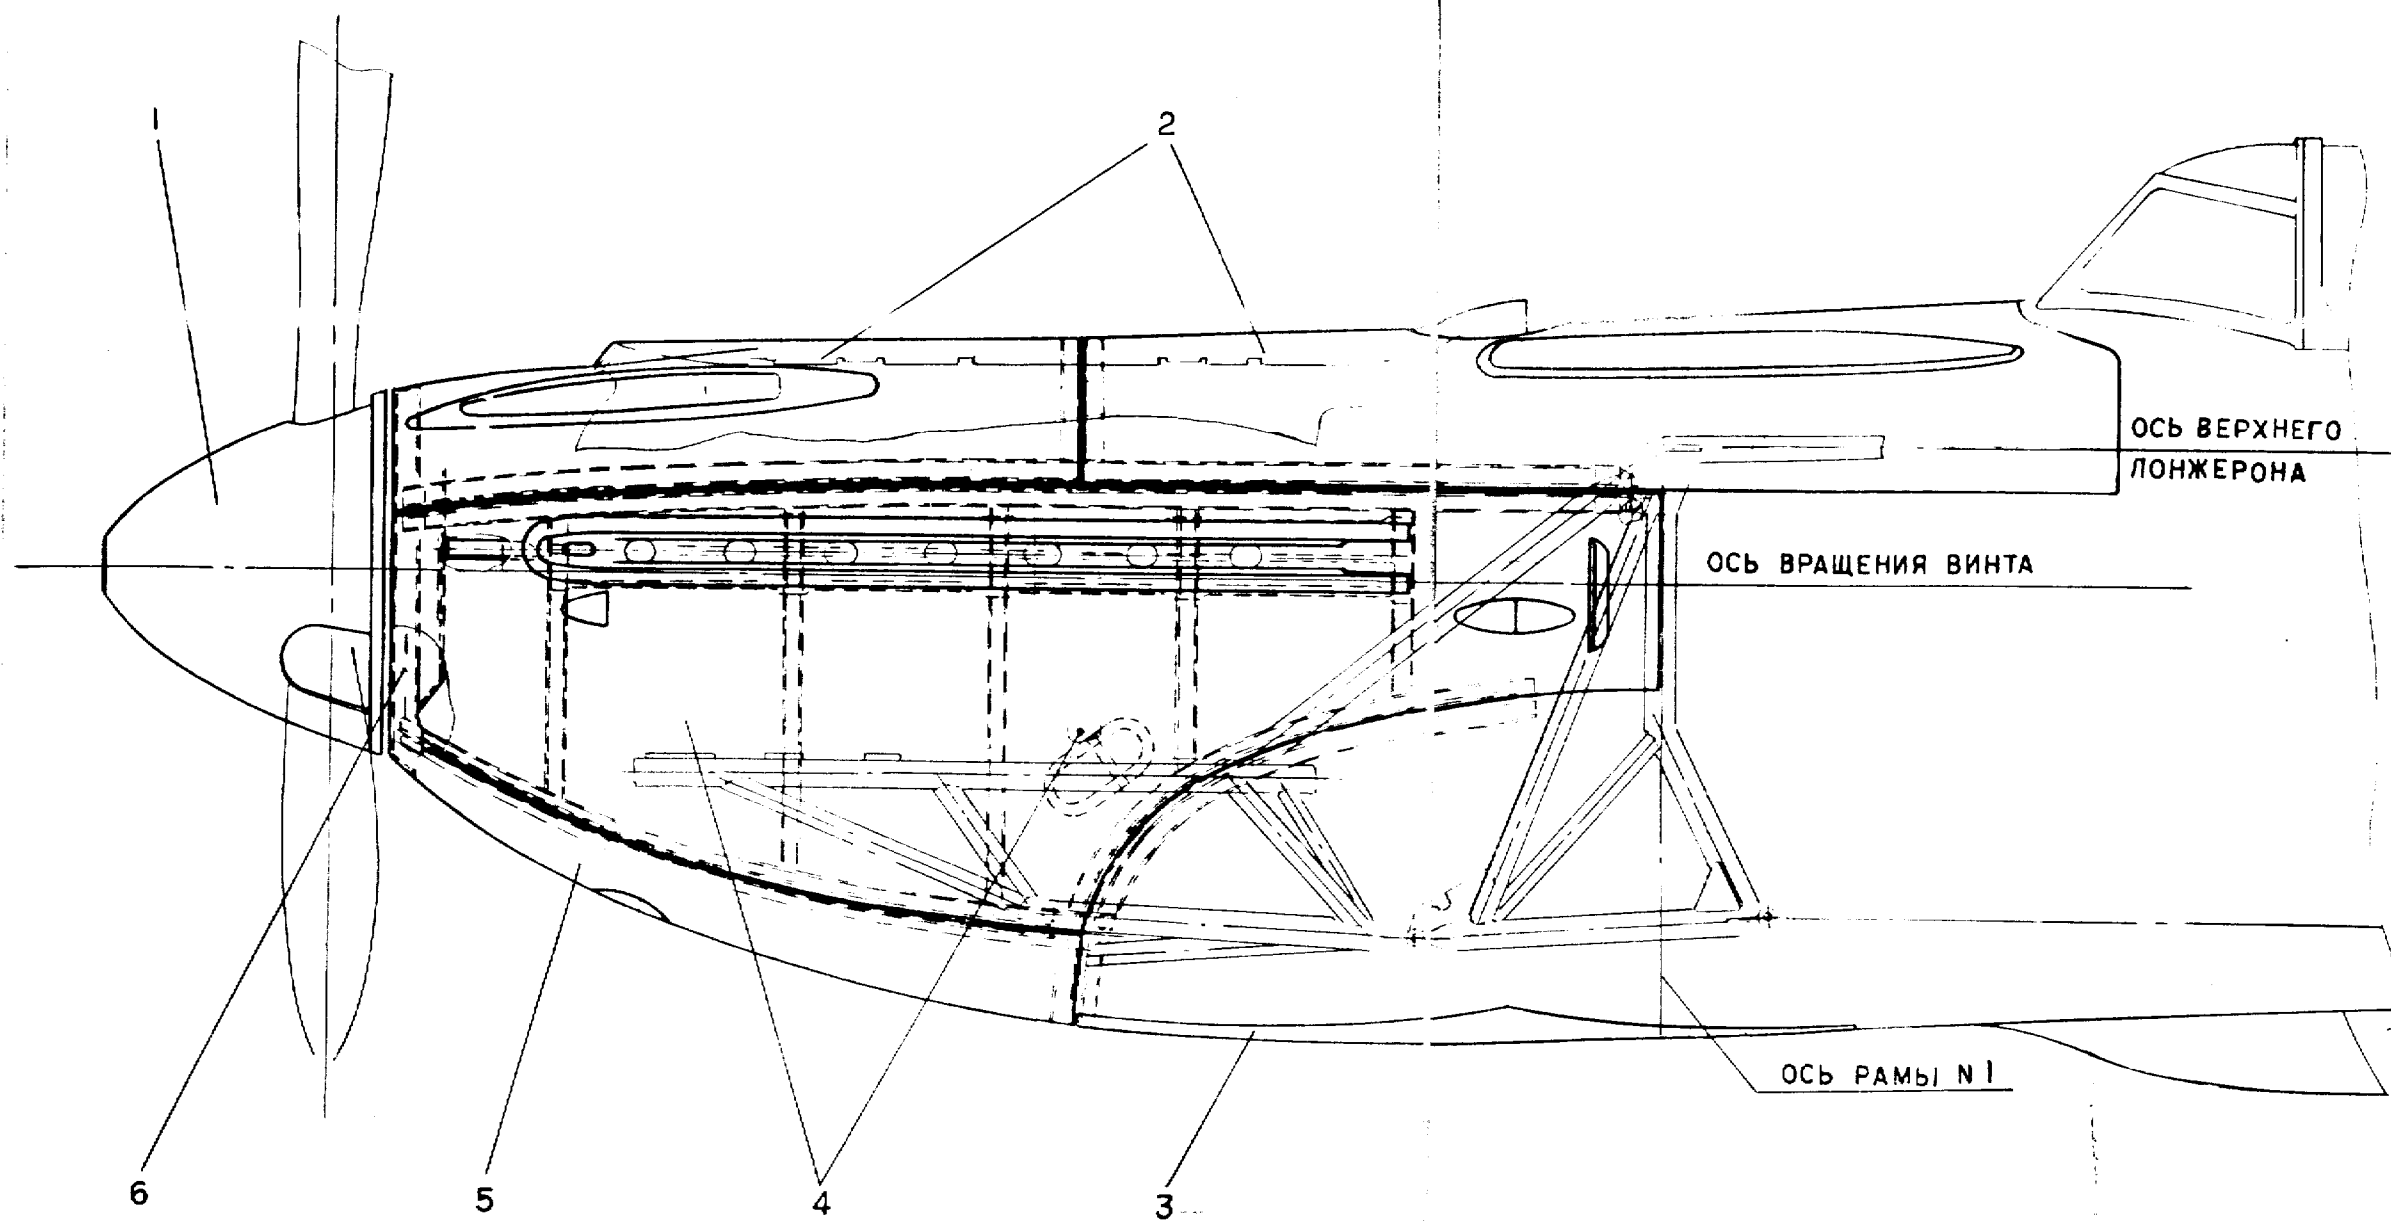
КАПОТ ДВИГАТЕЛЯ
